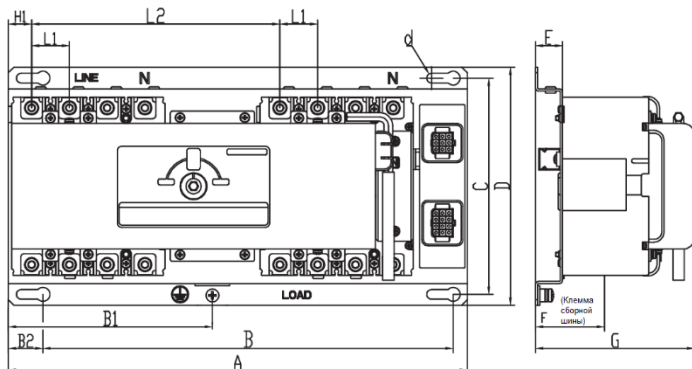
Габаритные размеры АВР-300 63-250А/3Р, 4Р в разъемном корпусе
